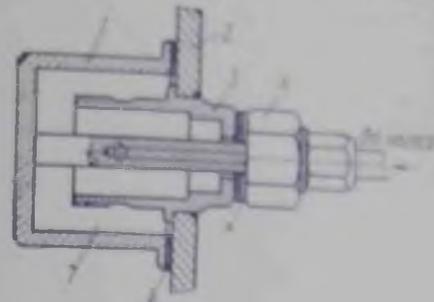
Приспособление для испытания обособленной части оболочки после ремонта
